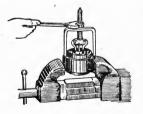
Съемник для выпрессовки подшинников из корпусов.
